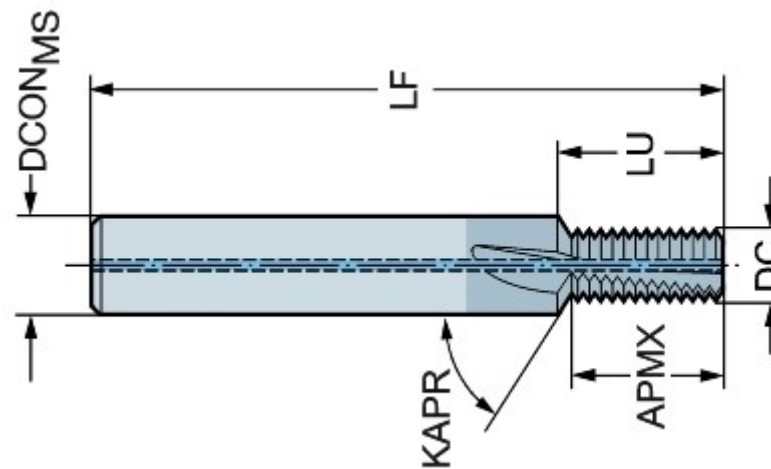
Різьбова фреза Coro Mill Plura R217.13C082150CC21K 1630
